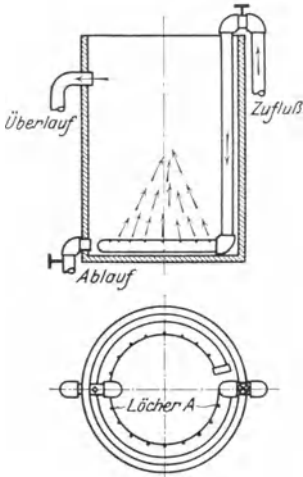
Kühlbad mit mittelbar zuzießendem Wasser.
